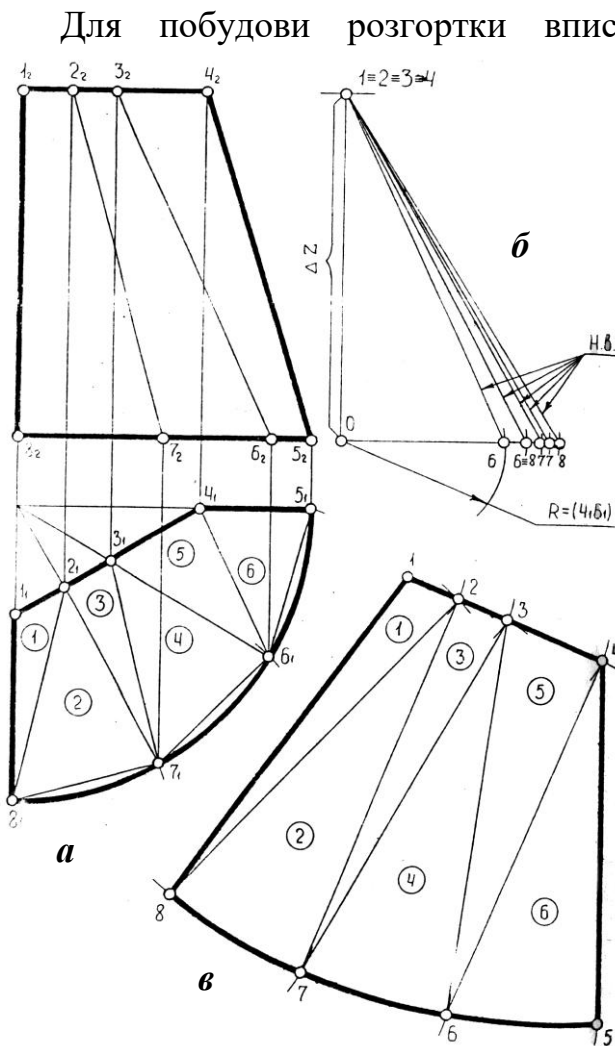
Побудова розгортки поверхні пропорційної розбивки .
